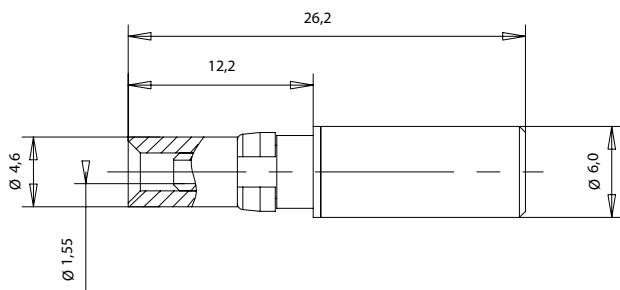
Zeichnung LWL-Steckverbinder Buchse
